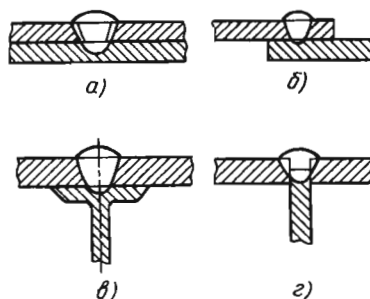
Схемы сварки электрозаклепочных и прорезных швов
